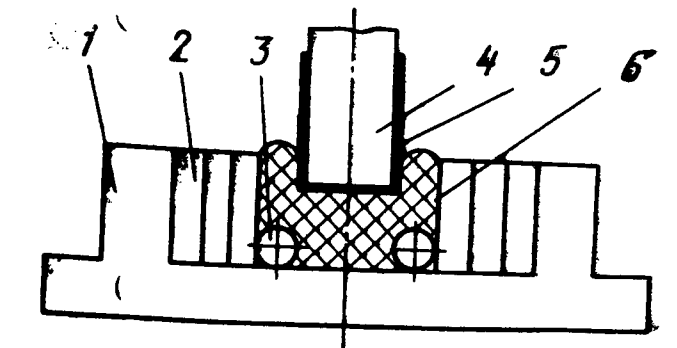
Универсальный гибочный штамп с полиуретановой матрицей
